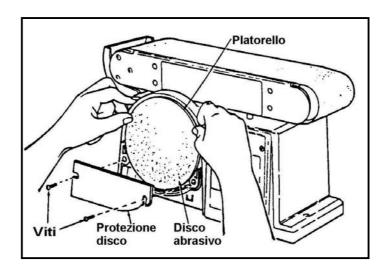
Montaggio del disco abrasivo Art. 0505.
